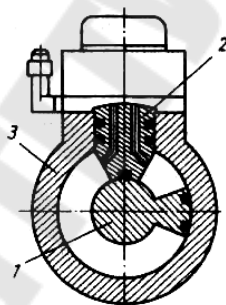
Схема неполноповоротного гидродвигателя типа «гидроквadrант»
